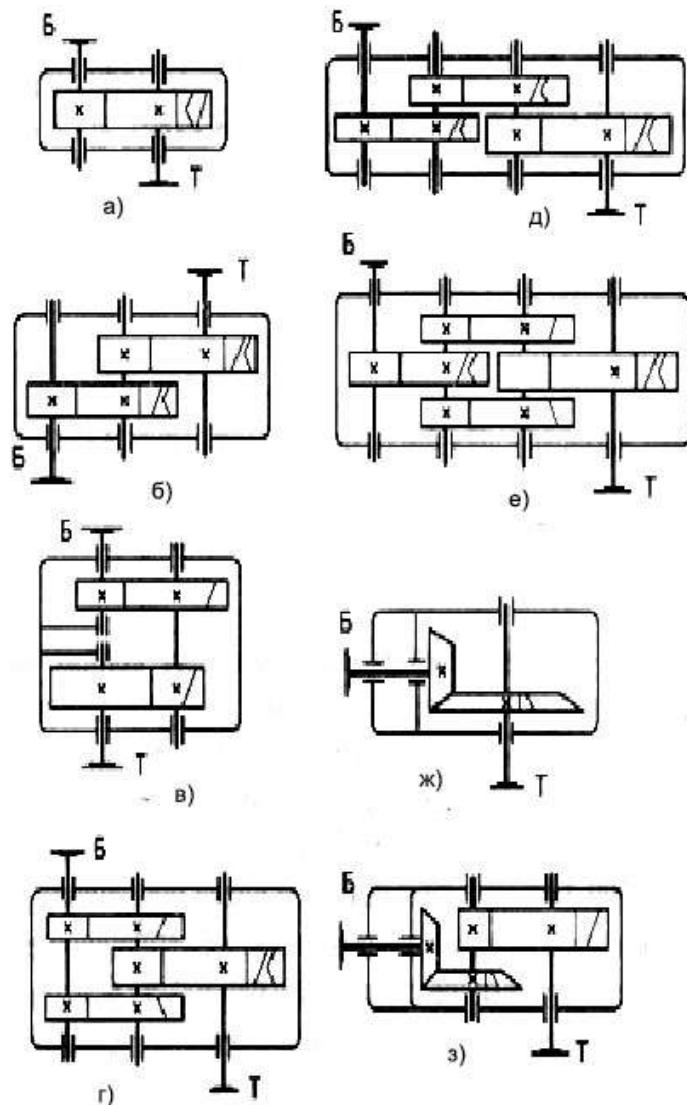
Наиболее распространенные схемы зубчатых редукторов: а — одноступенчатый; б — двухступенчатый развернутый; в — двухступенчатый соосный; г
